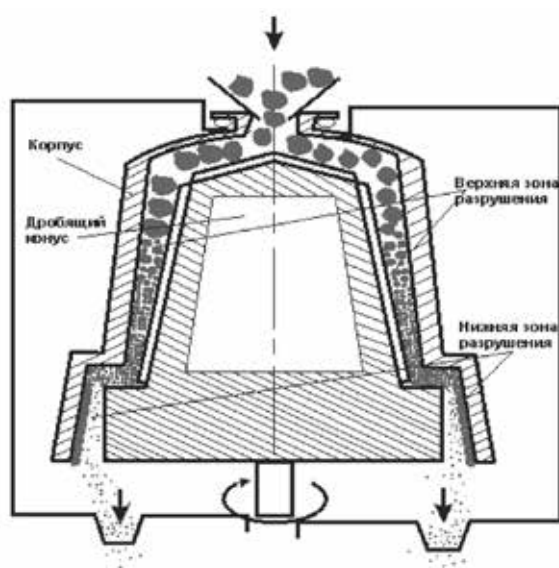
Схема конструкции конусной дробилки, общий вид лабораторной модели
